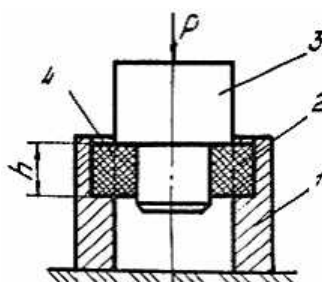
Схема испытания раструбного сварного соединения на сдвиг: 1 – матрица; 2 – кольцевой образец со сварным швом в центре стенки; 3 – пуансон; 4 – сварной шов
